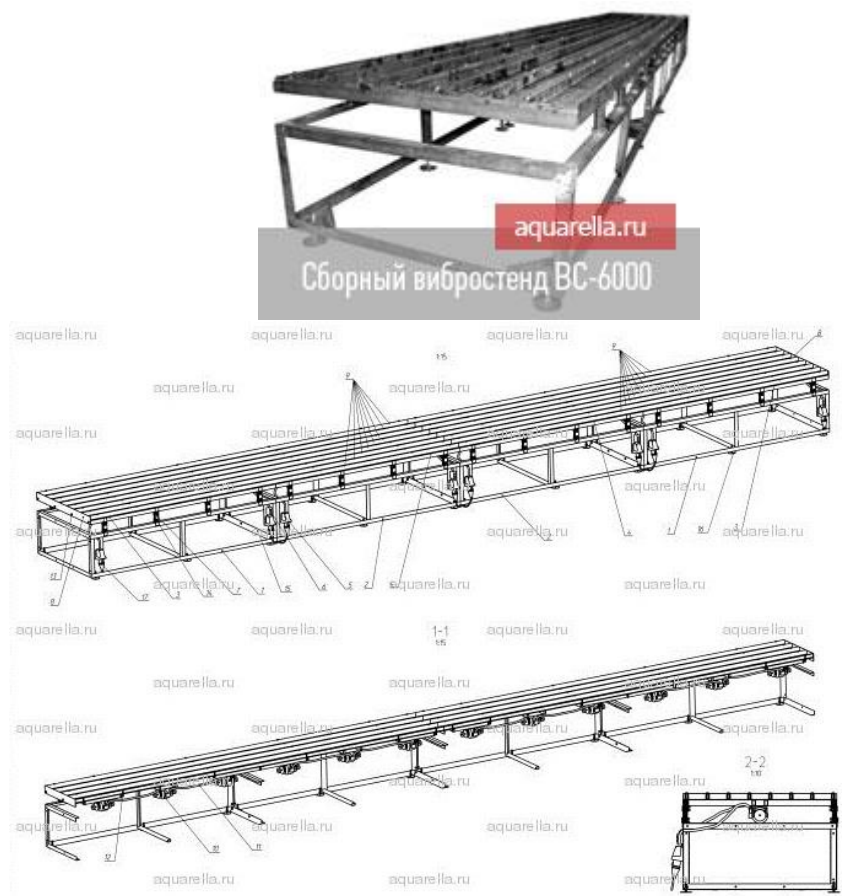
Сборный вибростенд для производства ж/б балок-перекрытий
